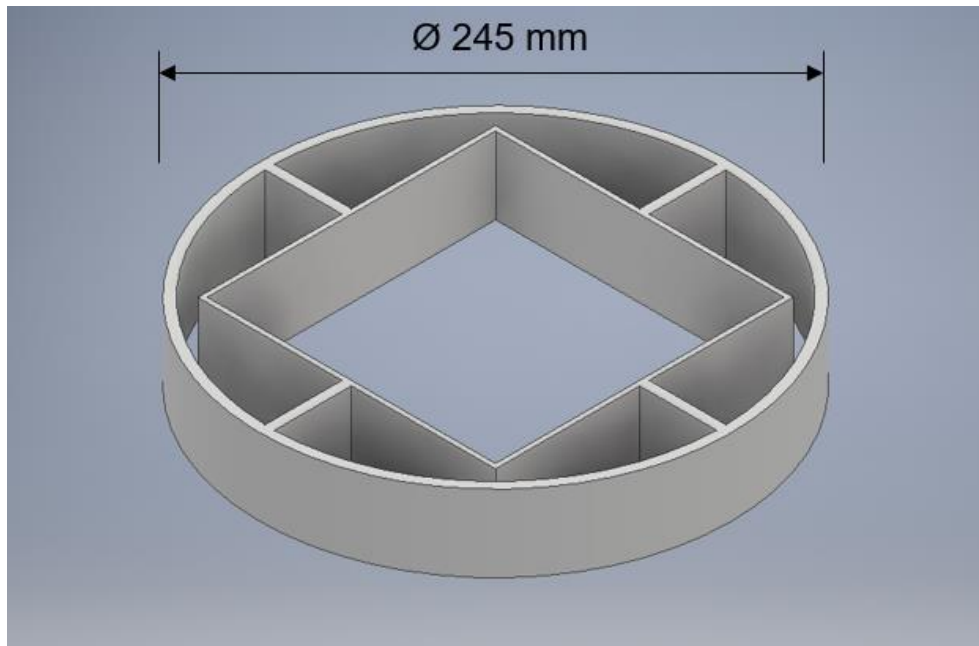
Esquema del perfil utilizado en la cimentación del Solar Tracker.
